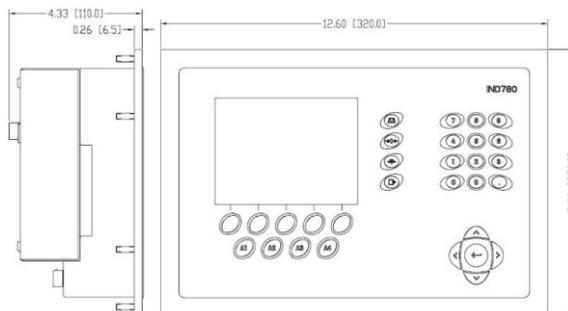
Dimensioni dell'armadietto con montaggio a pannello dell'IND780
